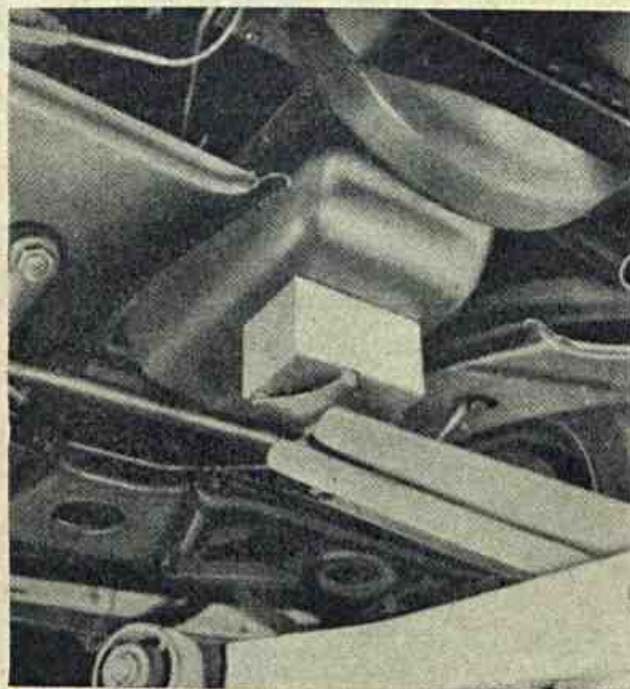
Um bloco de madeira debaixo do cárter de óleo do motor.
